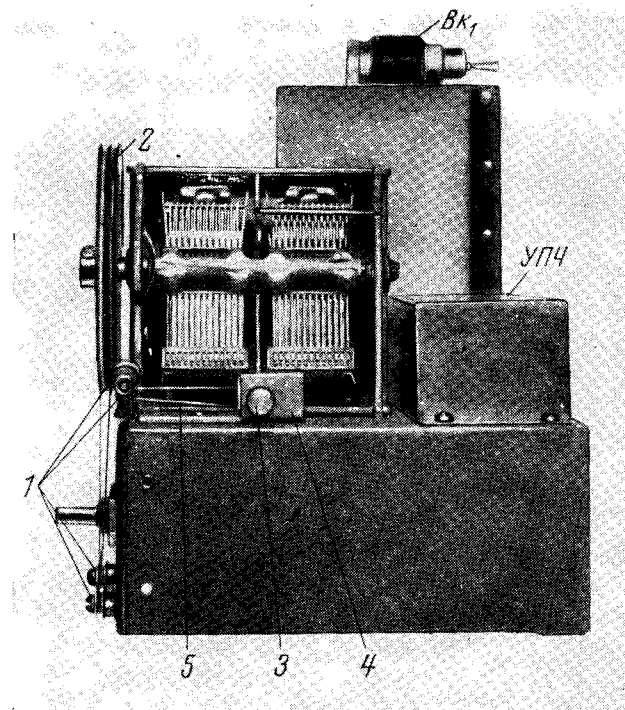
Верньерное устройство приемника (вид сбоку). Обозначения деталей верньерного устройства те же, что и на рис. 6.
